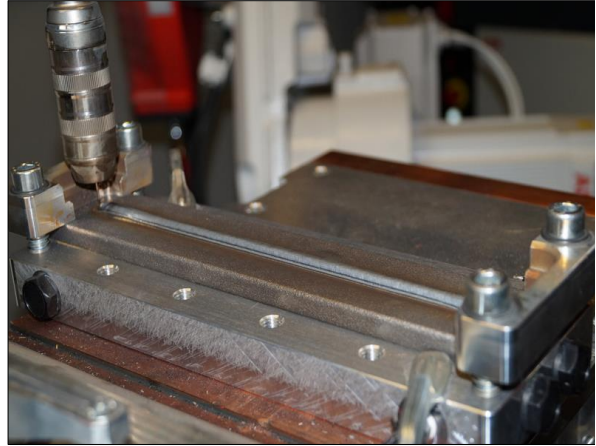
Wassergekühlter Schweißbisch
